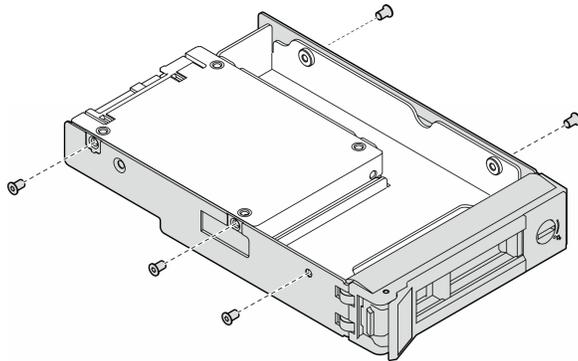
Entfernen der Schrauben, mit denen das 2,5-Zoll-Laufwerk und der Laufwerkadapter befestigt sind
